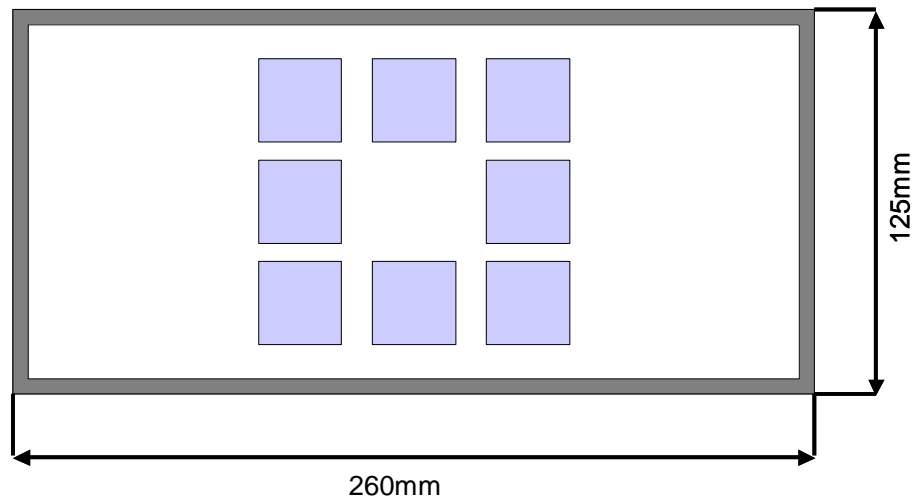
Schéma de principe du placement des composants sur la carte assemblée
